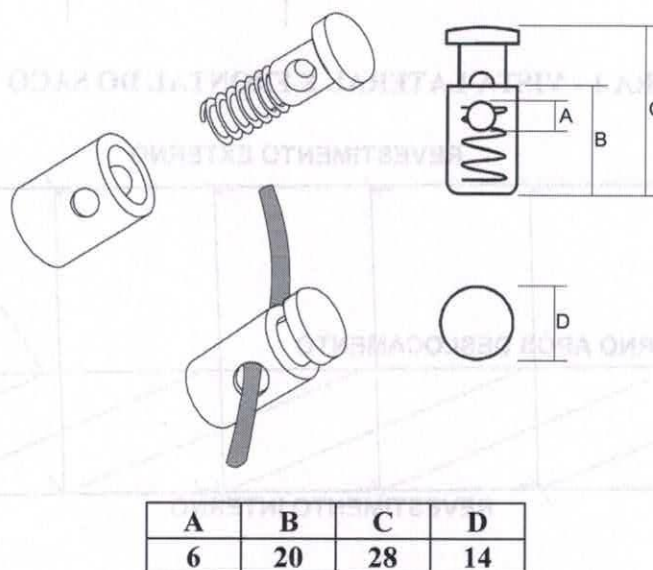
VISTA DA PRESILHA COM MOLLA (MEDIDAS EM MM)
